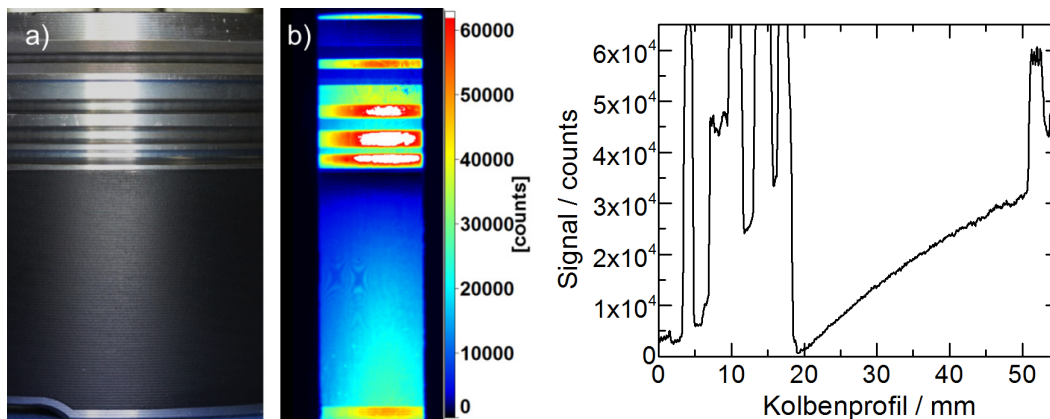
a) Seitenansicht Kolbens, b) LIF-Bild des Kolbenprofils ohne Kolbenringe
